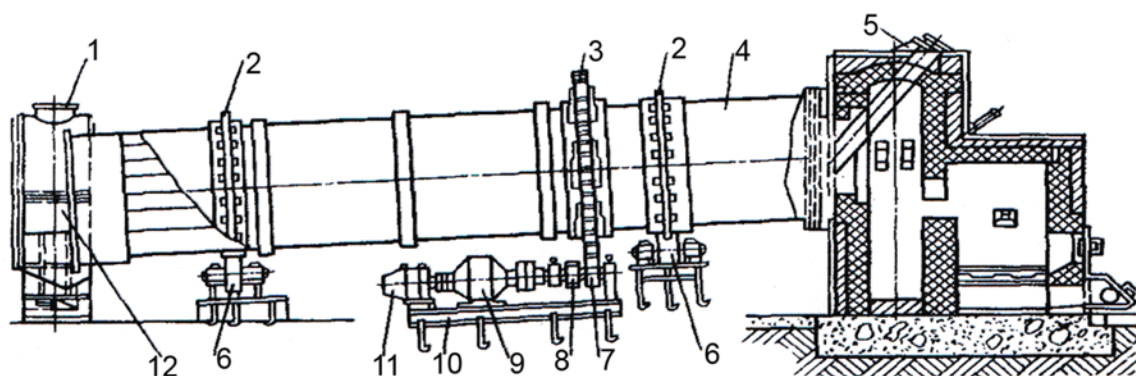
Вращающаяся печь: 1 – патрубок; 2 – бандаж; 3 – венцовая шестерня; 4 – сварной стальной цилиндр; 5 – загрузочная течка; 6 – опорный ролик; 7 – подвенцовая шестерня; 8 – зубчатая пара; 9 – редуктор; 10 – сварная плита; 11 – электродвигатель; 12 – разгрузочная камера
